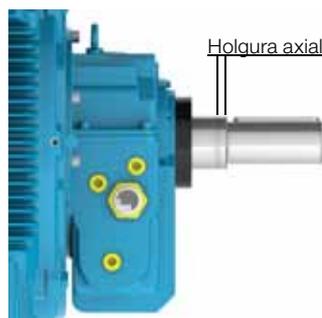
Holgura axial en motor equipado con cojinete de deslizamiento.
